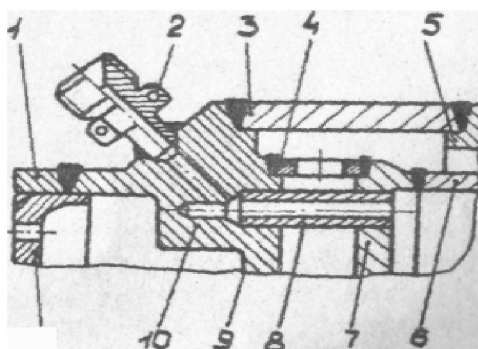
Схема соединения головки с корпусом камеры: 1 - газовод, 2 - штуцер для измерения давления газа в камере, 3 - соединительное кольцо. 4 - кольцо с радиальными отверстиями, 5 - рубашка корпуса камеры, 6 - стенка корпуса, 7 - внутреннее днище головки, 8 - втулка, 9 - среднее днище, 10 - корпус головки, 11 - газораспределительная решетка
